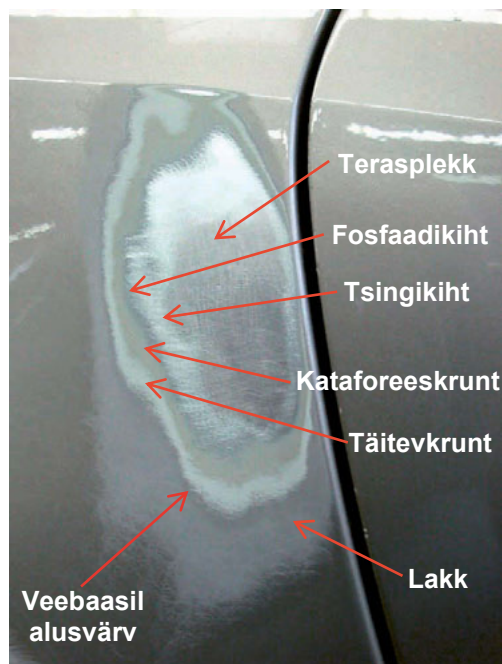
Auto originaalvärvkatte (OEM) kihid
